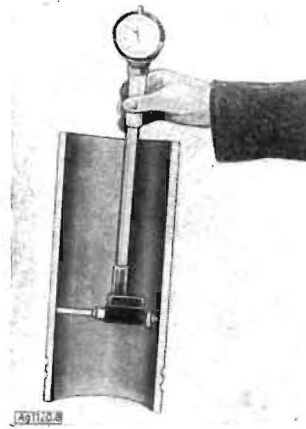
Messung des Durchmessers der Buchse mit Indikator-Innenmesser
